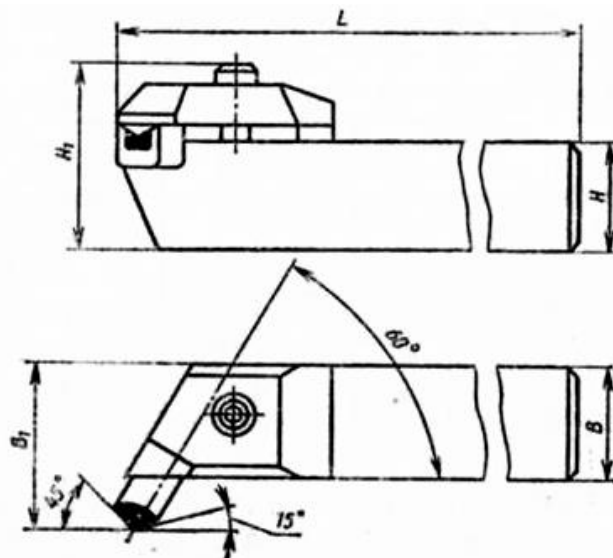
Расточной резец для сквозных отверстий с косым креплением вставки с режущей пластиной из СТМ
